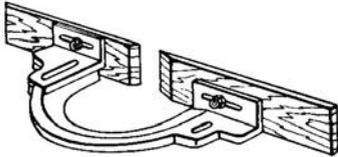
Anschlaglineal für Arbeiten an der Fräsmaschine.
